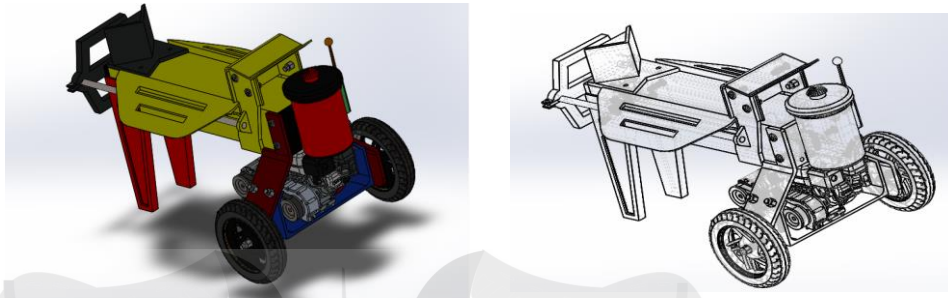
Diseño completo de la cortadora hidráulica de leñas accionada por un motor Otto
